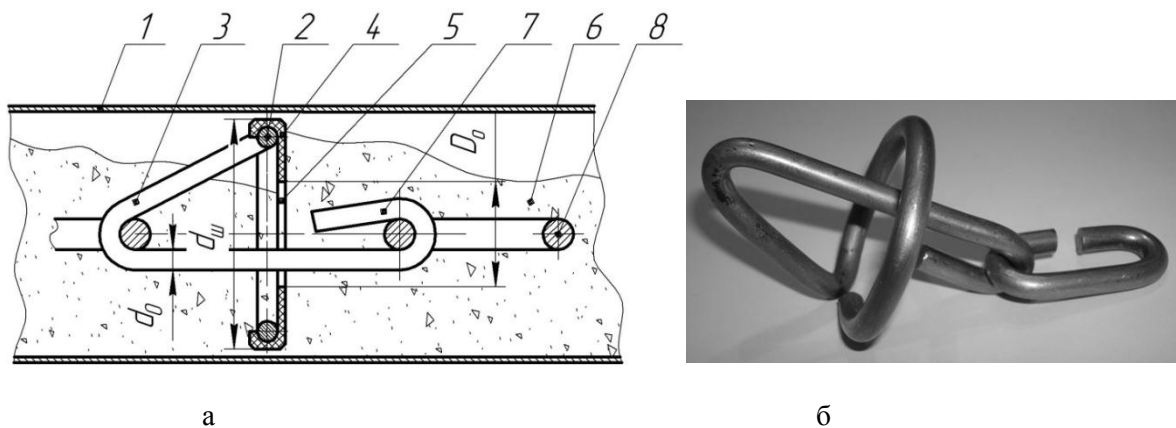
Конструкція секційного скребкового робочого органу транспортера-змішувача:
